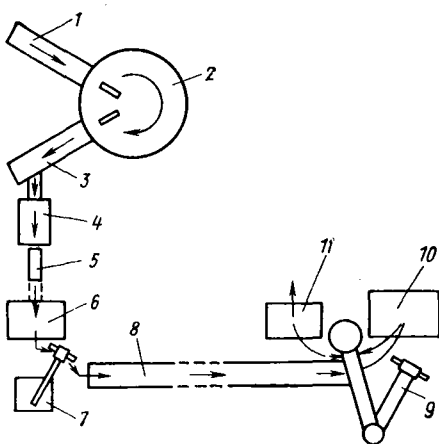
Схема механизированной линииковки коленчатых валов на заводе фирмы Бофорс: 1 — автоматическое загрузочное устройство; 2 — вращающаяся печь; 3 — устройство разгрузки поковок; 4 — окалиносниматель; 5 — автоматическое загрузочное устройство; 6 — молот предварительной обработки; 7 — манипулятор с ручным управлением; 8 — цепной конвейер; 9 — гидравлический робот; 10 — молот окончательной обработки; 11 — обрубной пресс
